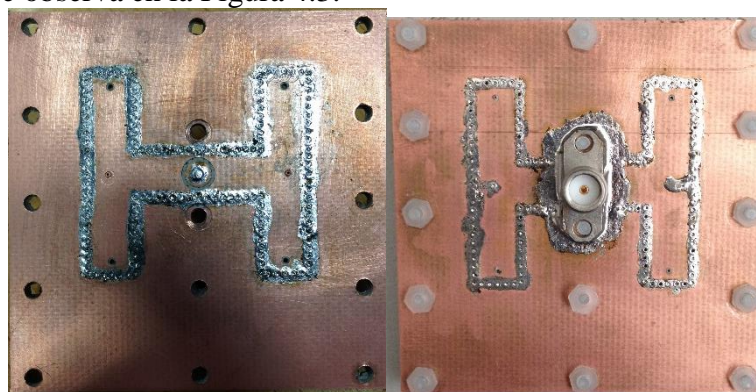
Aspecto de las caras superior (izda) e inferior (dcha) de la red SIW tras soldar.
